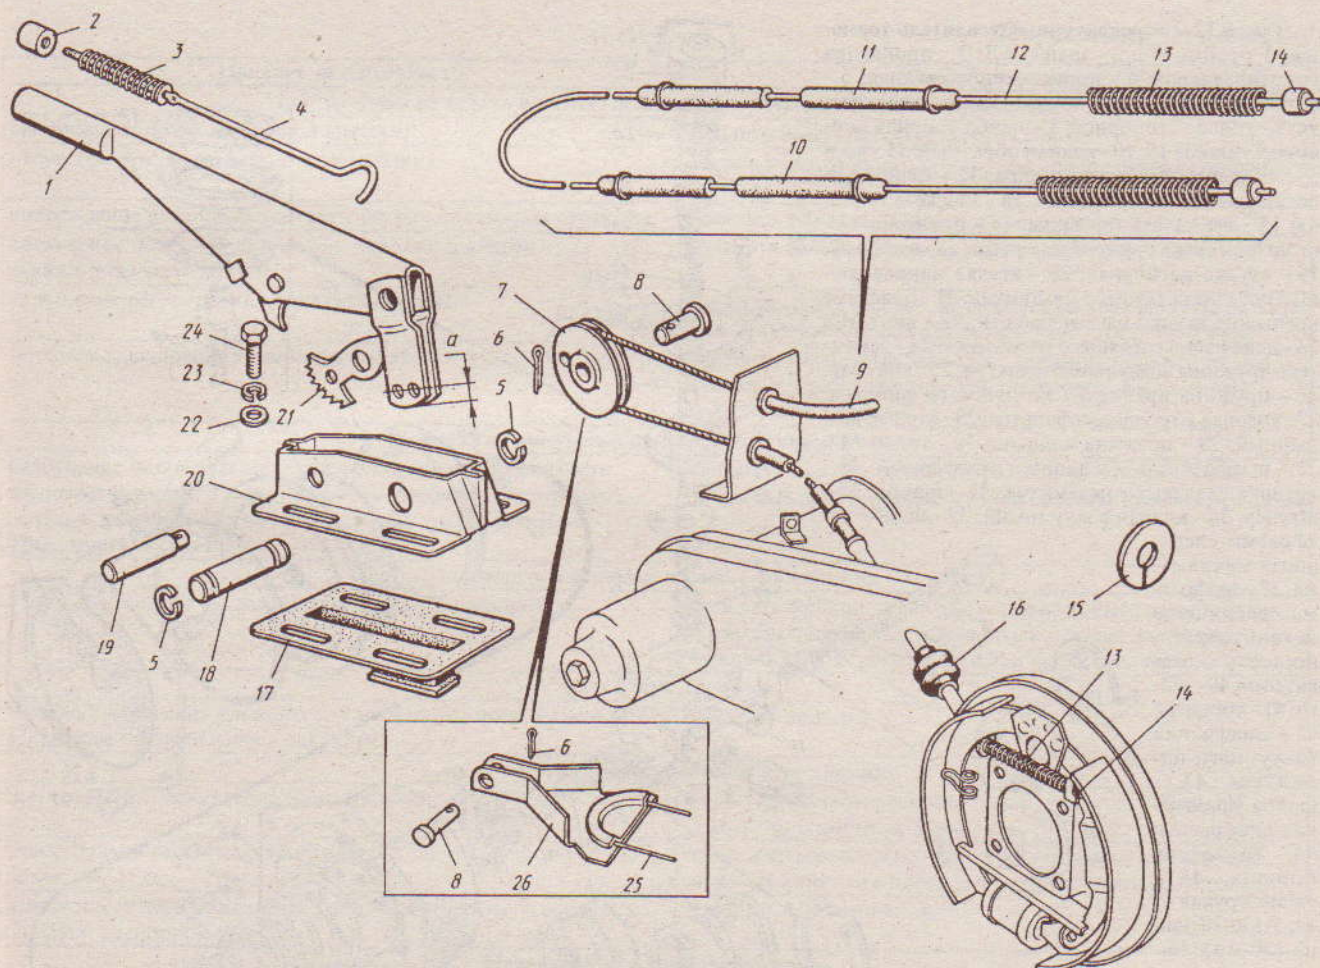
Рычаг и трос привода стояночного тормоза: 1 - рычаг в сборе; 2 - кнопка рычага; 3 - пружина; 4 - стержень кнопки рычага; 5 - кольцо стопорное; 6 - шплинт 3,2x12; 7 - ролик (с 10.92 г.); 8 - палец 8x20; 9 - трос в сборе (с 10.92 г.); 10 - оболочка троса в сборе левая длиной 765 мм; 11 - оболочка троса в сборе правая длиной 820 мм; 12 - канат 3,1 - Г - В - Н - 1960 длиной 2835 мм; 13 - пружина троса; 14 - наконечник; 15 - шайба упорная пружины троса; 16 - чехол защитный; 17 - чехол рычага; 18 - ось; 19 - ось сектора рычага; 20 - кронштейн крепления рычага; 21 - сектор; 22 - шайба 8; 23 - шайба 8Л; 24 - болт М8; 25 - трос ручного привода в сборе; 26 - кронштейн-уравнитель троса (по 10.92 г.)
